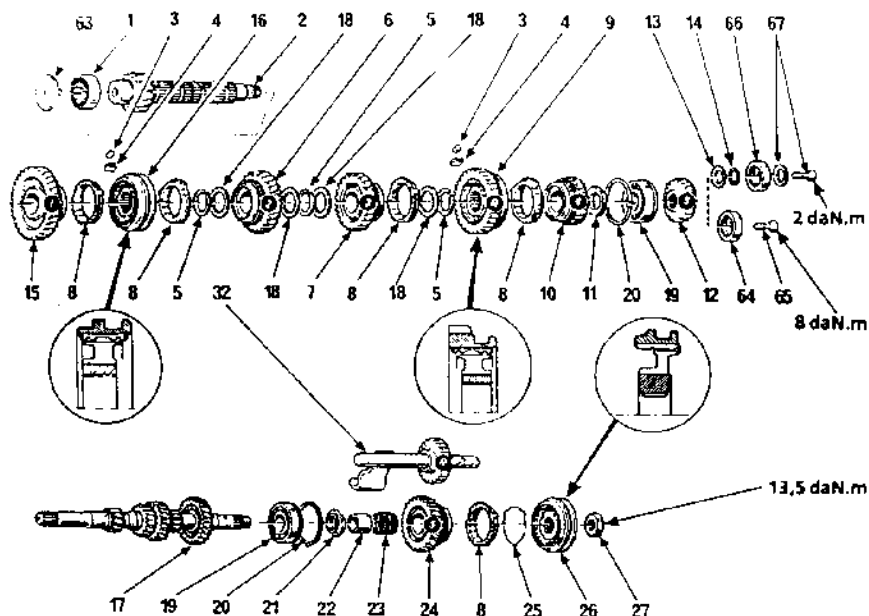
WEWNĘTRZNY MECHANIZM ZMIANY BIEGÓW
